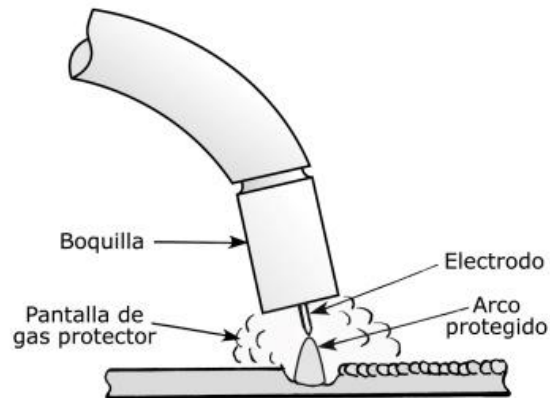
Esquema de soldadura por cordón (Rodríguez, 2001).
